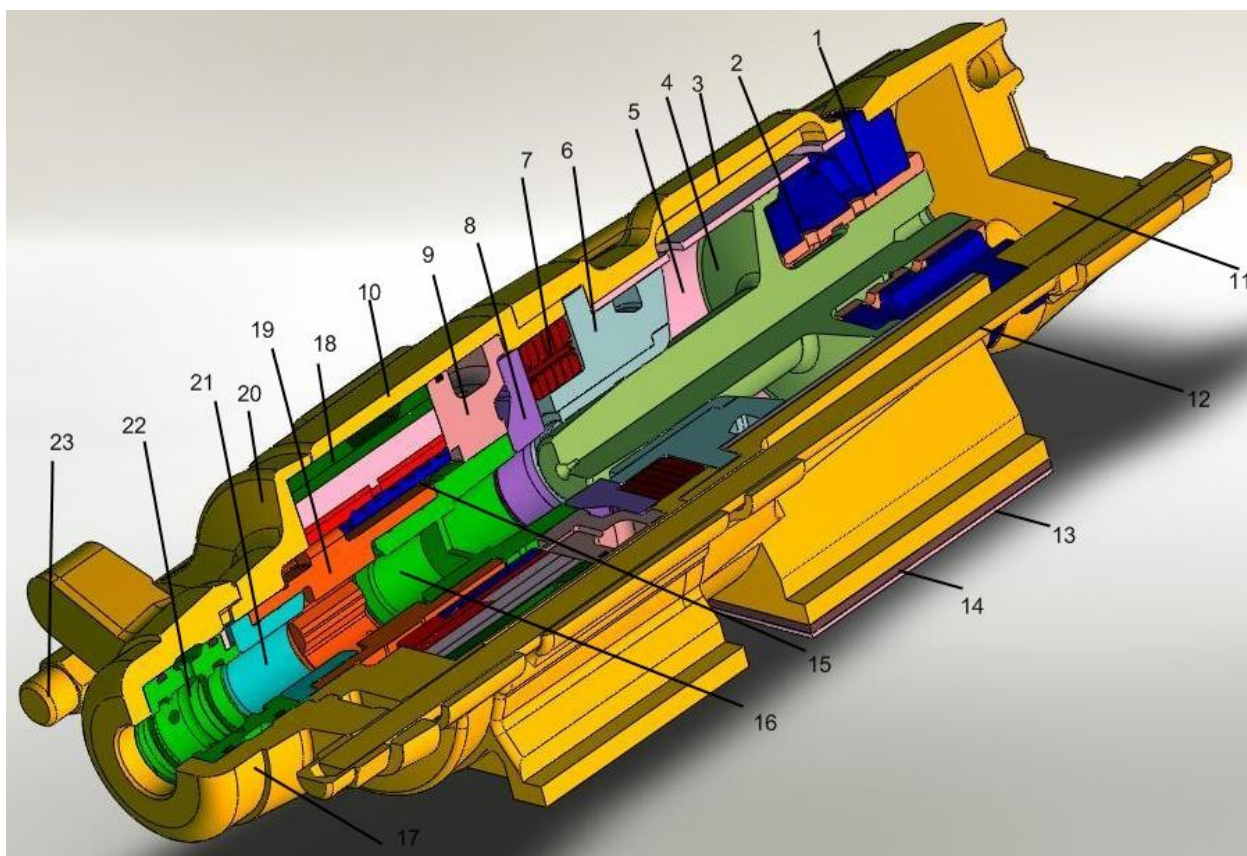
Бурова головка 501А: 1 - втулка; 2 – корпус; 3 – корпус; 4 – поршень; 5 – гільза; 6 – втулка; 7 – демпфер; 8 – п'ята; 9 – диск; 10 – корпус; 11 – кришка; 12 – болт; 13 – кришка; 14 – пластина; 15 – золотник; 16 – опора; 17 – кришка; 18 – статор; 19 – шпindelь; 20 – кришка; 21 – втулка; 22 – муфта; 23 – гайка.
